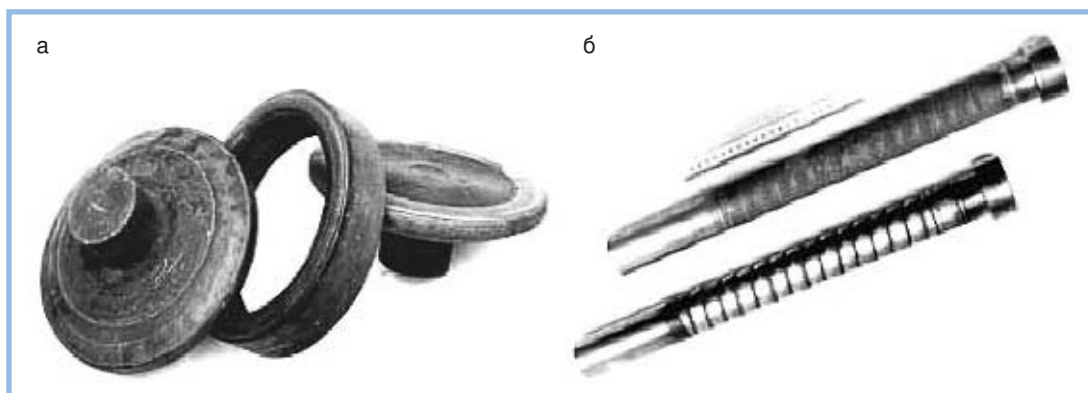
Внешний вид деталей задвижек для гидротранспортировки угля, наплавленных плазменно-порошковым способом: а — детали затвора; б — штоки
